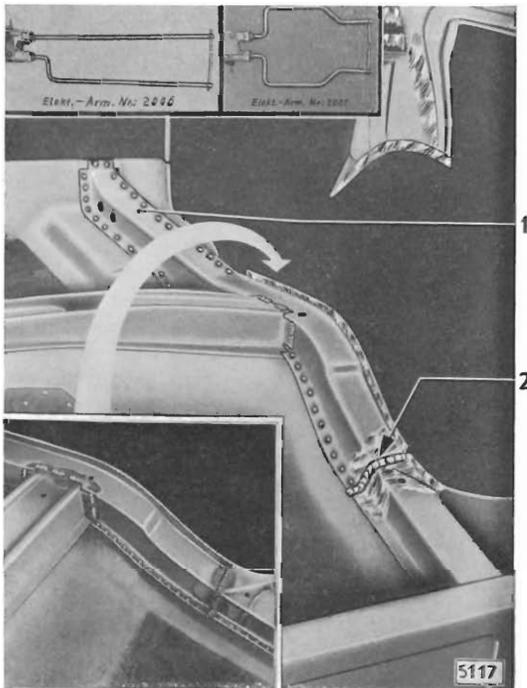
Angeschweißter Hinterlängsträger
